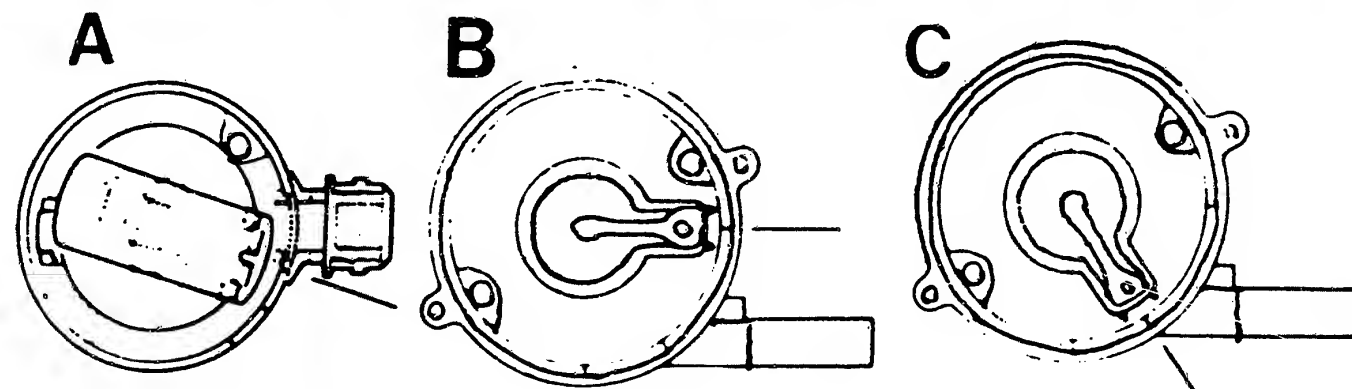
Stellung des Rotors zum Verteilergehäuse im Zündzeitpunkt des 1. Zylinders bei den verschiedenen Motortypen: A = 1,8 und 2,0l Vergasermotoren – B = 2,0l Einspritzmotor – C = 2,8l-V6-Motor.
